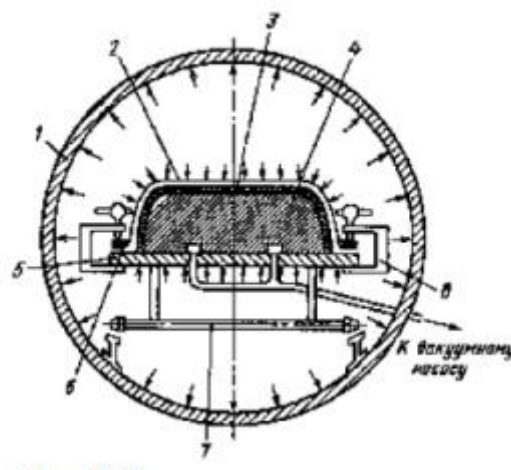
Схема вакуумно-автоклавного формування деталей з
